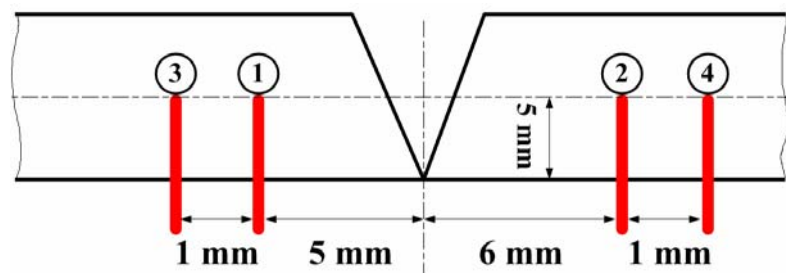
Disposition des thermocouples sur la maquette de soudage.
